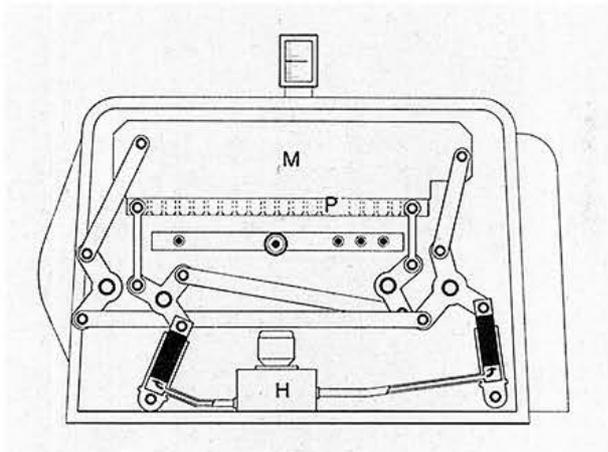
Schneidemaschine mit hydraulischem Antrieb des Preßbalkens und des Messers:
